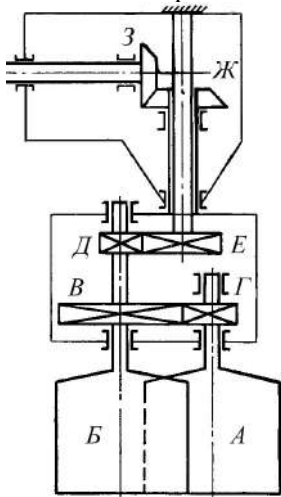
Кинематическая схема смесителя 6-ЛС с обозначением мест, где имеют место потери на трение: *А, Б* – лопасти (трение в подшипниках); *В* – зацепление зубчатых колес; *Г* – внутренний подшипник лопасти *А*; *Е* – зацепление зубчатых колес; *Д* – подшипники планетарного редуктора; *Ж* – пара конических зубчатых колес; *З* – подшипники хобота.
